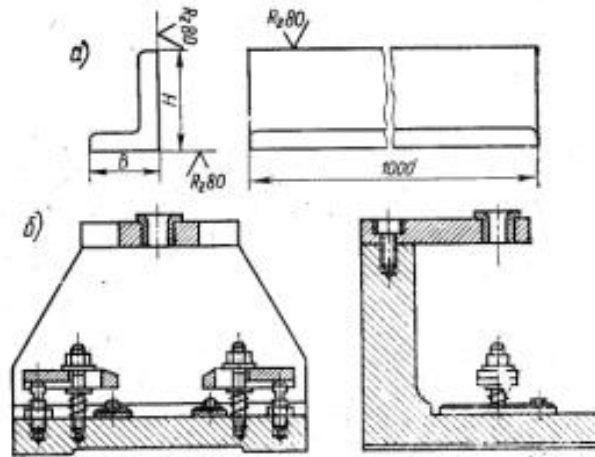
Заготовка корпусу пристосування з кутника (а) і використання його в пристосуванні (б)
